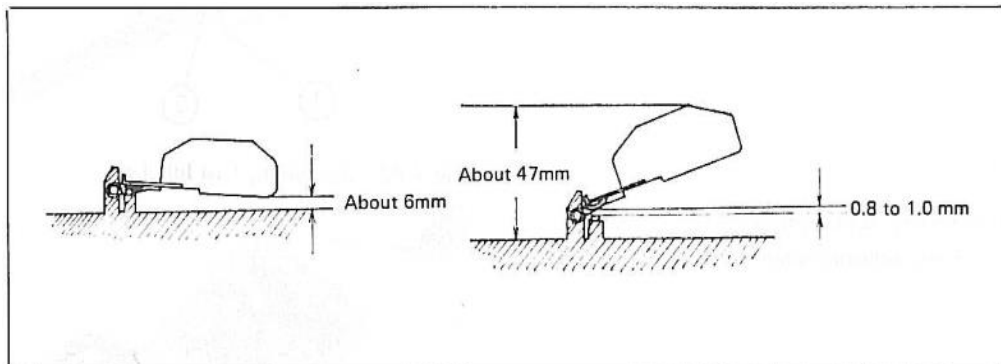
Checking Air Horn / Kepala karburator
